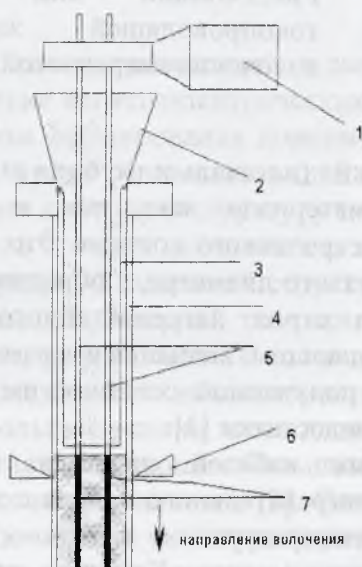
Схема засыпки порошковой изоляцией кабельной заготовки с использованием ультразвуковых колебаний: 1-магнитострикционный преобразователь, концентратор, 2 - бункер, 3 - направляющая труба (шток), 4 - труба-заготовка, 5 - направляющие трубки для жил, 6 - вибратор, 7-токопроводящие жилы.
